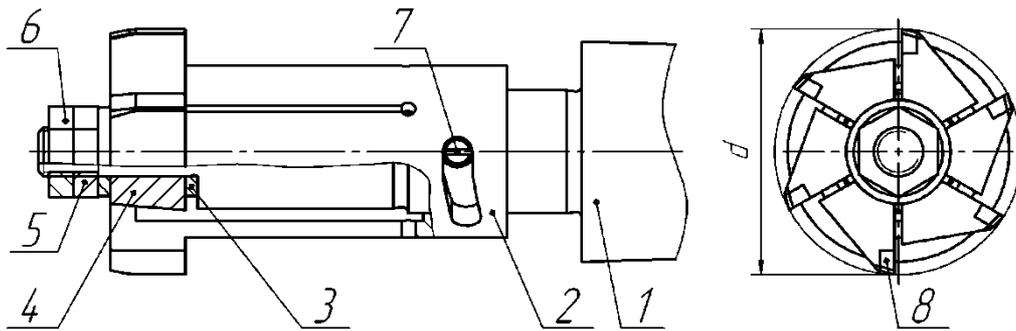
Развёртка для бесрисочного вывода из обработанного отверстия детали
